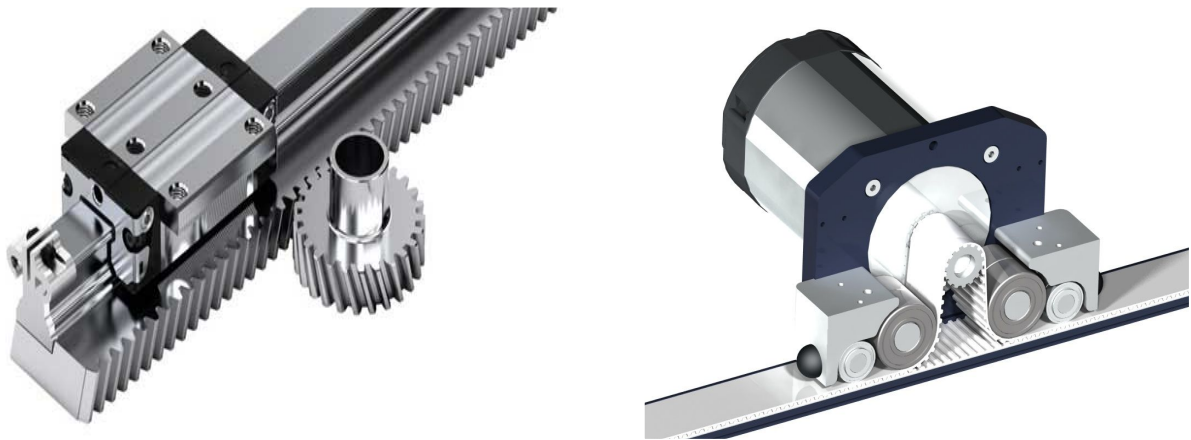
Передача руху за допомогою зубчатої рейки та зубчата пасова передача
